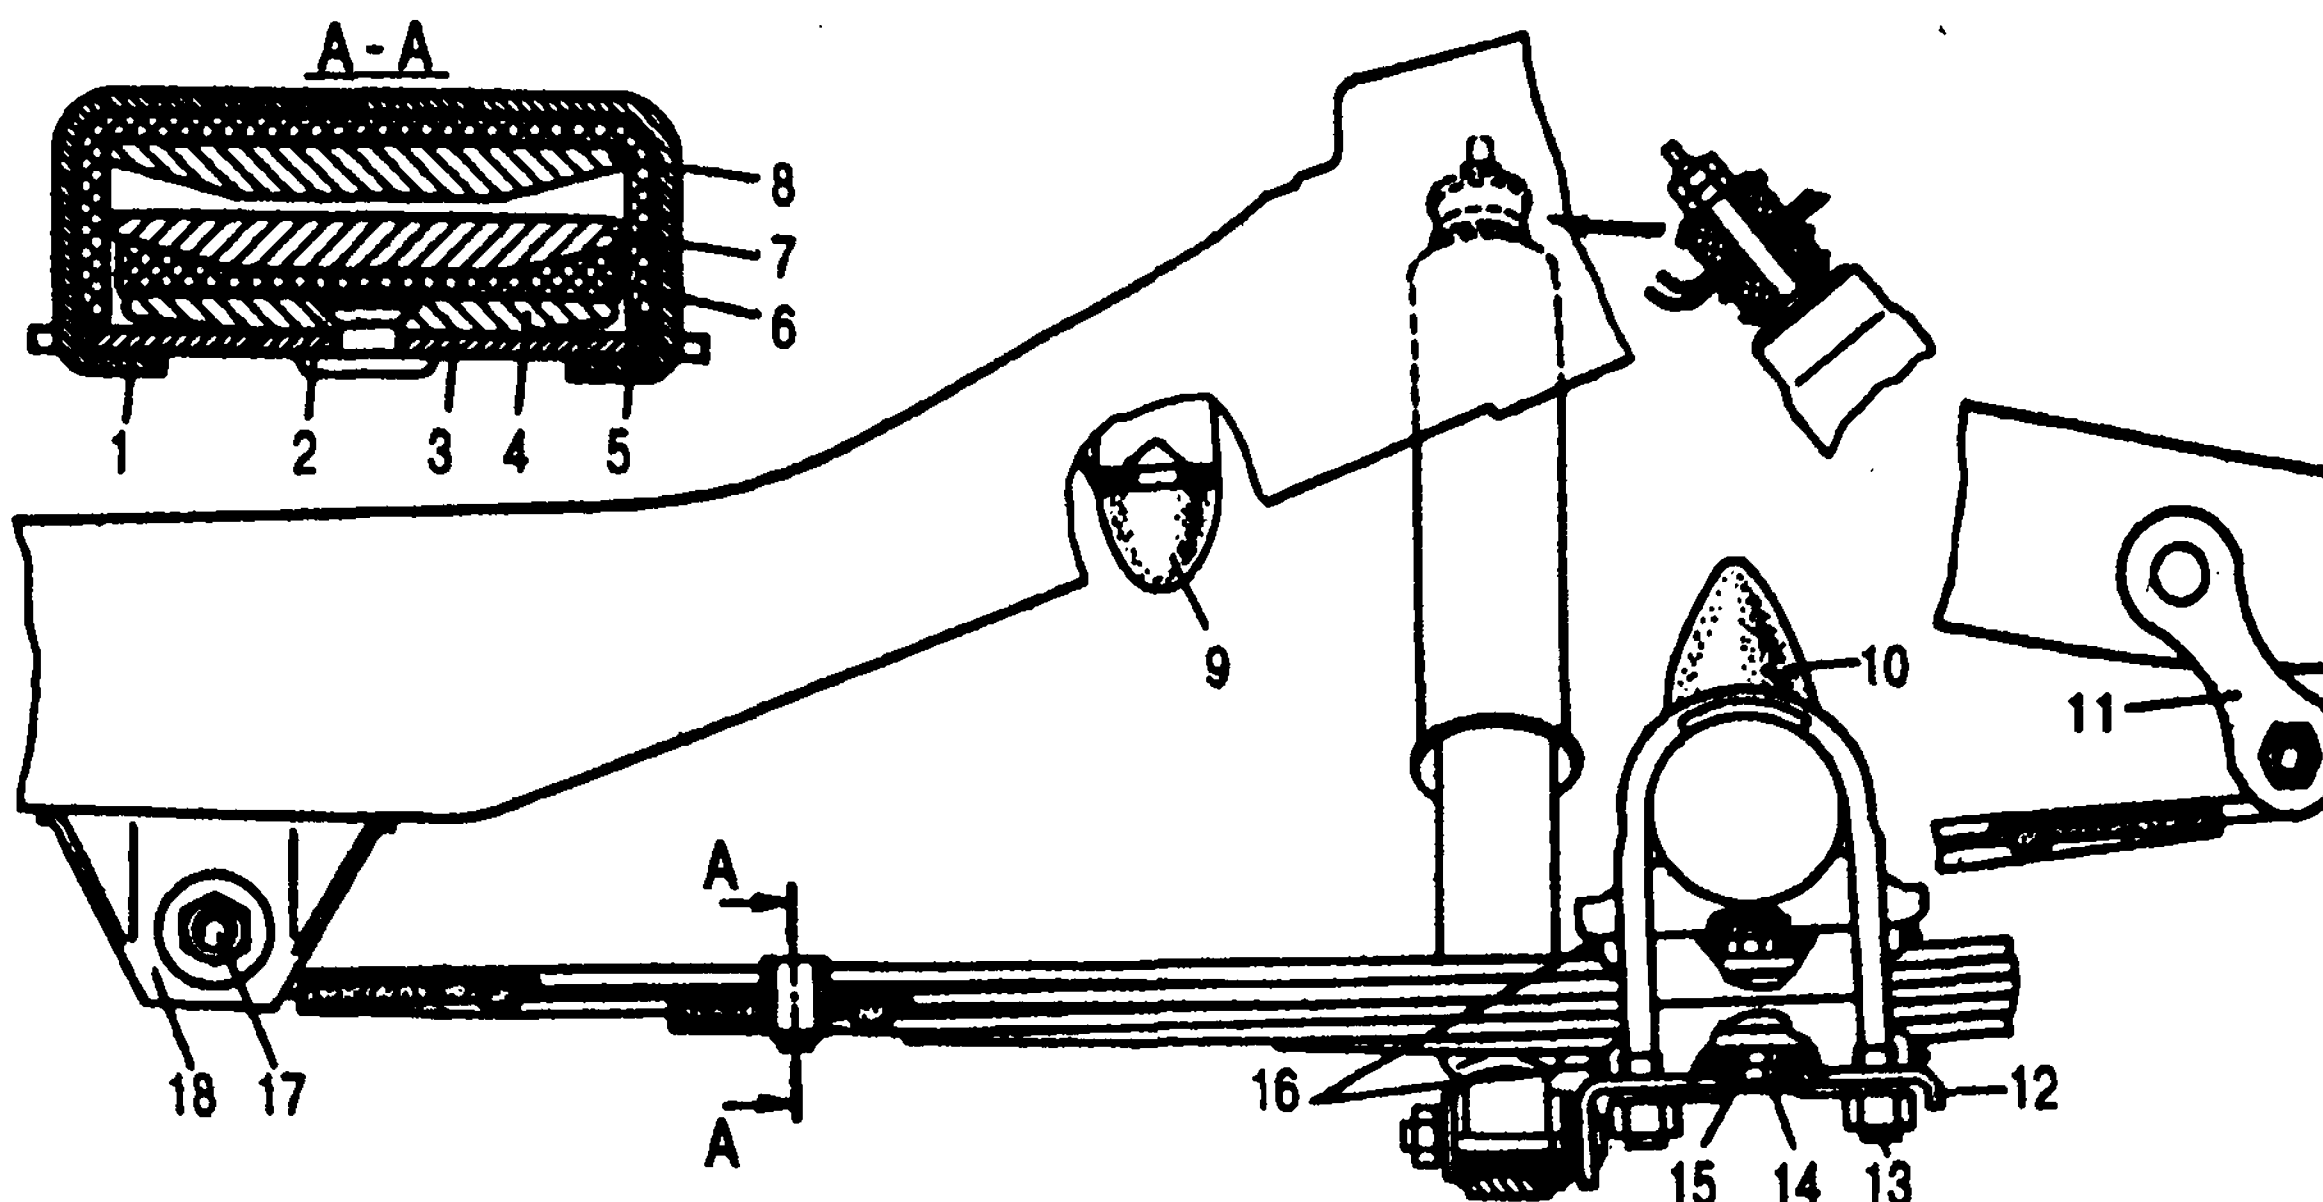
Задняя подвеска: 1 - коренной лист; 2 - второй лист рессоры; 3 - прокладка; 4 - прокладка; 5 - третий лист; 6 - пластина хомута; 7 - заклепка; 8 - хомут; 9 - кронштейн; 10 - палец; 11 - дополнительный буфер; 12 - обойма; 13 - резиновые подушки; 14 - центральной болт; 15 - стремянка; 16 - подкладка рессоры; 17 - буфер; 18 - серга
